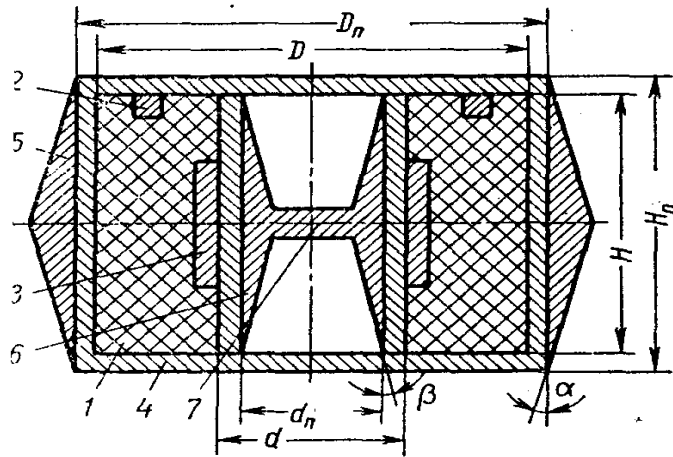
Креслення деталі і поковки з припусками і допусками:
